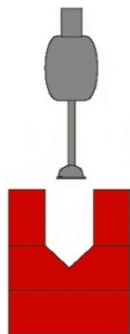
Das Werkzeug in die Bohrung einfahren, möglichst nahe an die Kreuzung.
